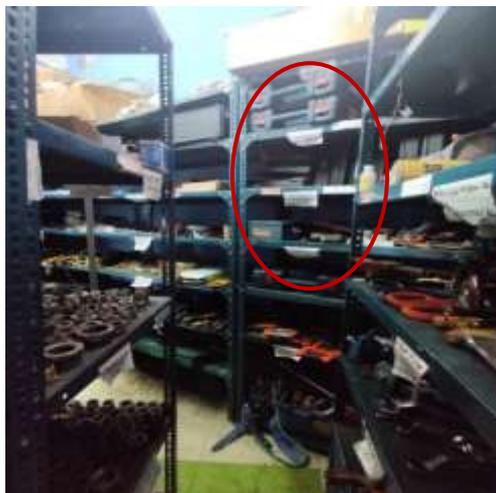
Codificación de las estanterías metálicas de la bodega del DM
